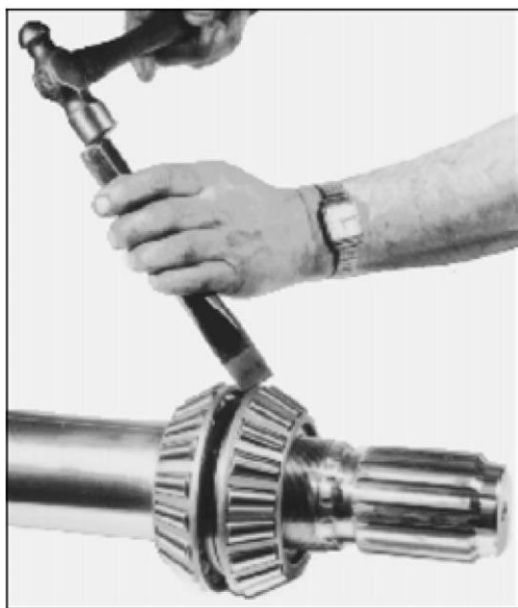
Используйте стамеску, чтобы срезать сепараторы подшипника для извлечения роликов.
